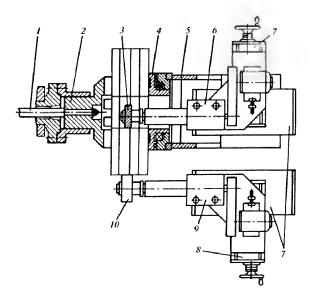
Схема станка модели РТ-103 после модернизации (вид сверху):
